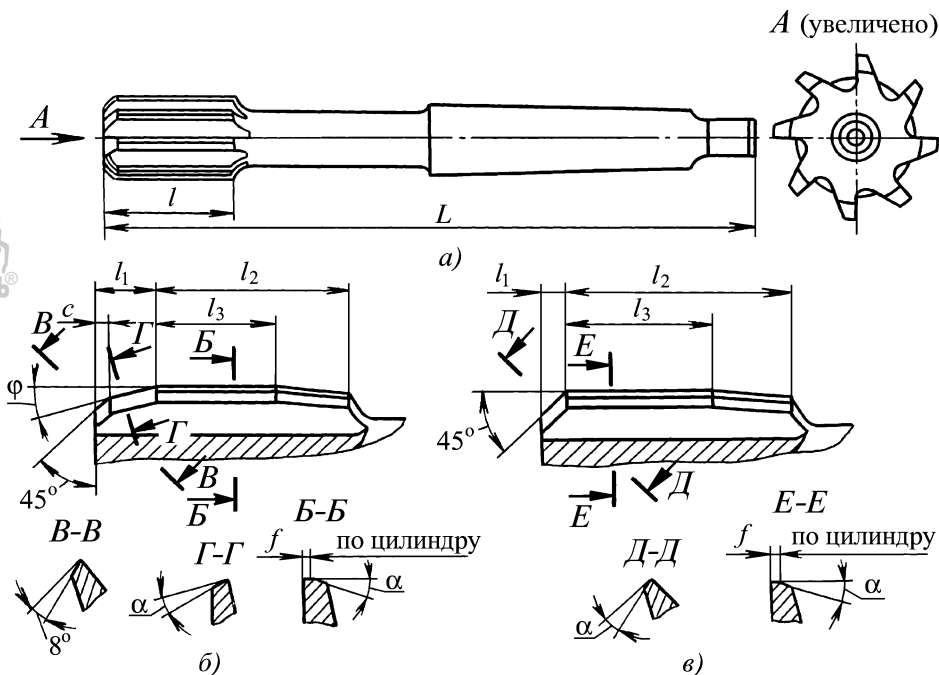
Конструктивные элементы (а) и элементы режущей части развертки (б, в)
